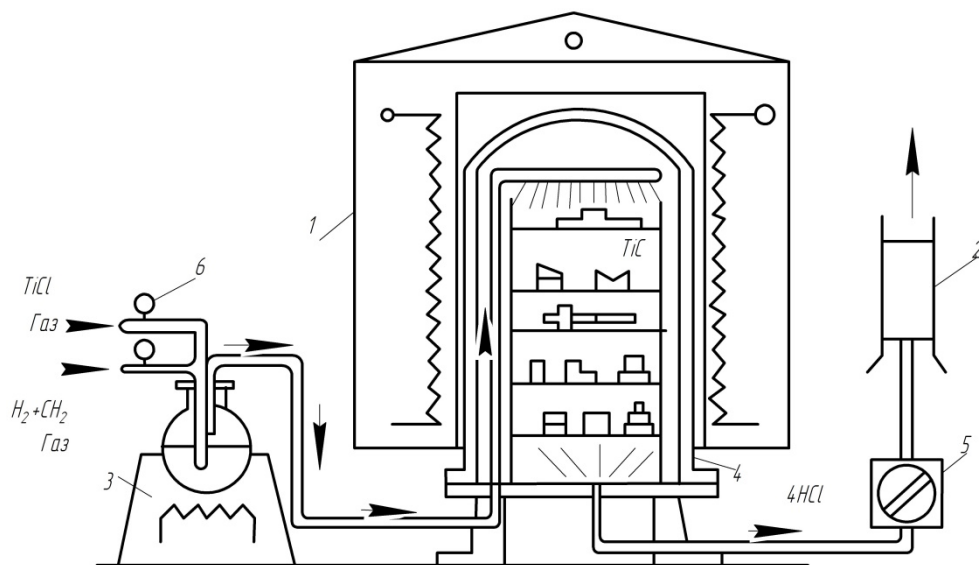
Схема установки для нанесення покриття газофазним способом:
